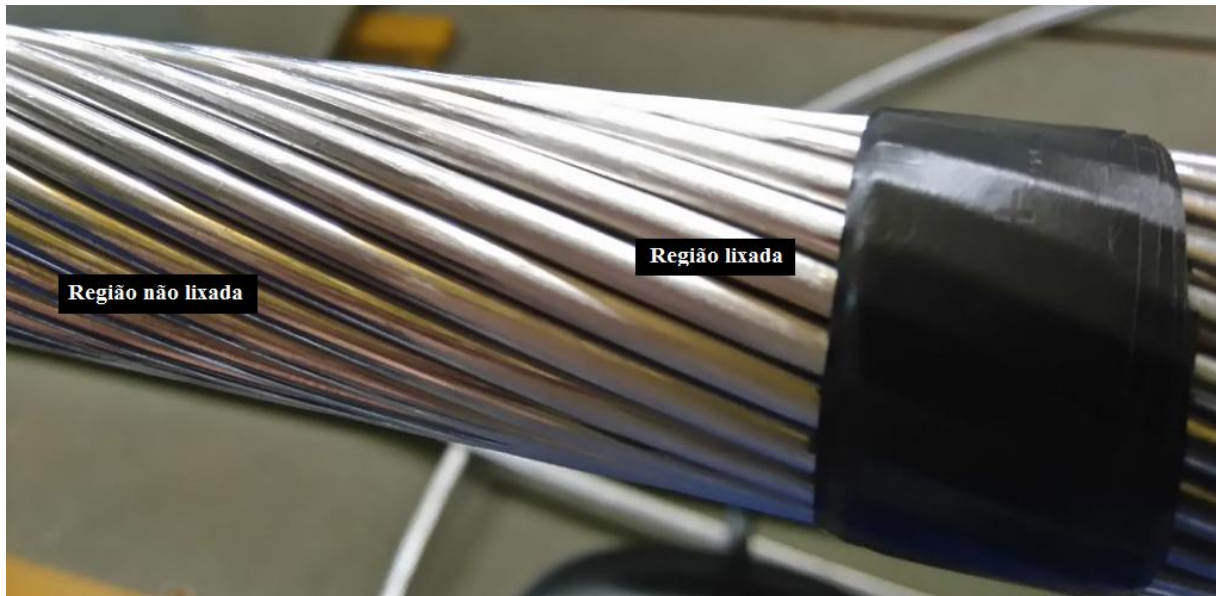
Preparo da camada externa do cabo para colagem dos extensômetros.
